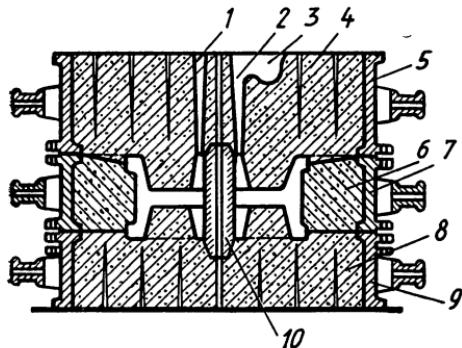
Форма для отливки шкива, изготовленная в трех опоках:
